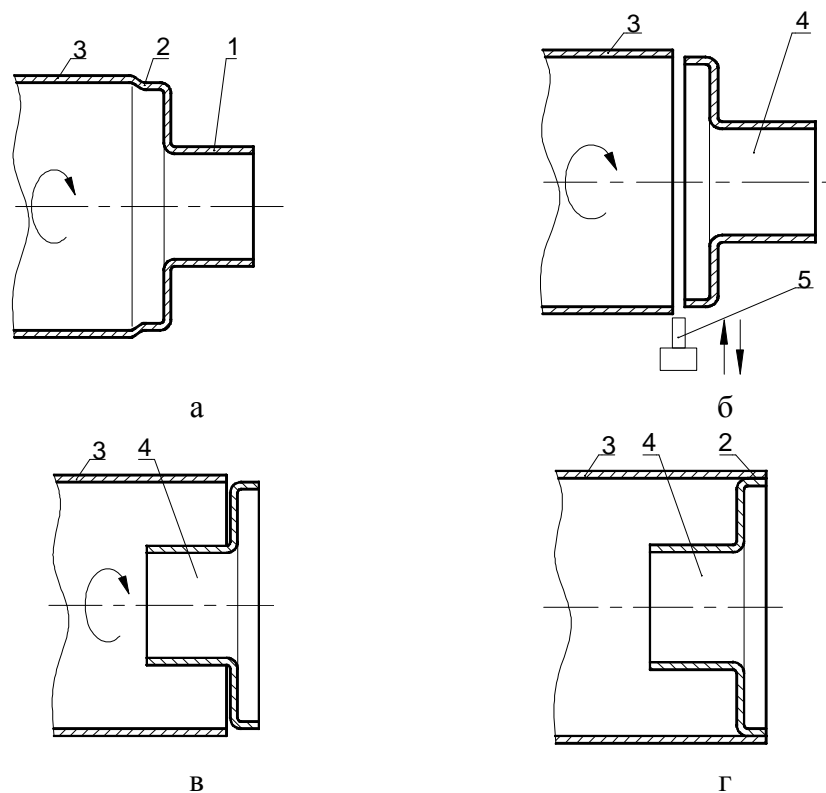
Способ получения трубчатой заготовки методом выворота внутрь пластическим деформированием:
